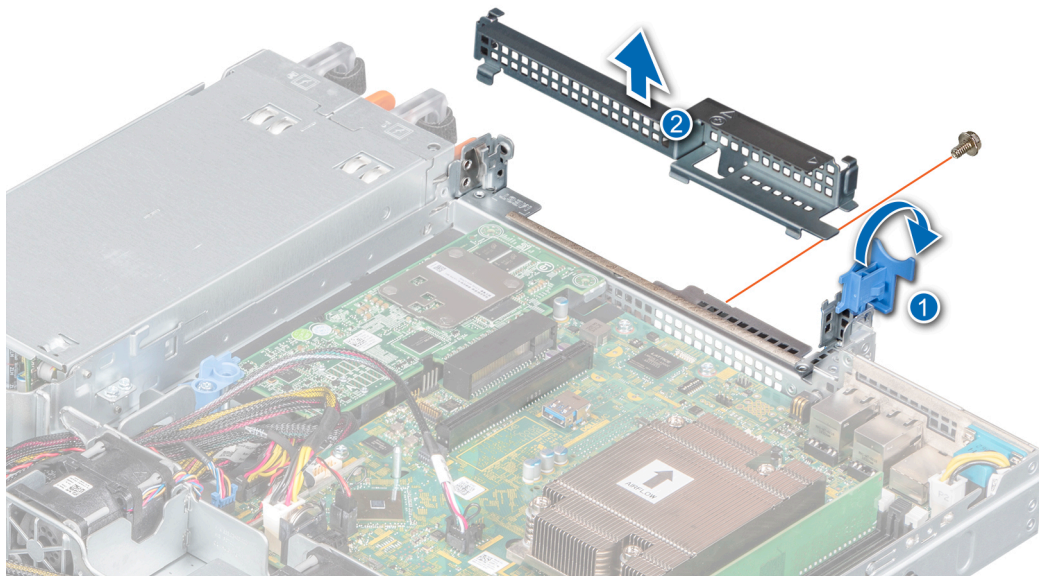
Retrait de la plaque de recouvrement de la carte de montage pour carte d'extension
